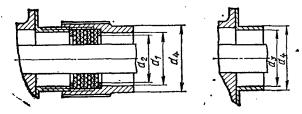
Подключение кабеля с резиновой или пластиковой оболочкой для двигателей с $h=280 \div 355\,$ мм.
